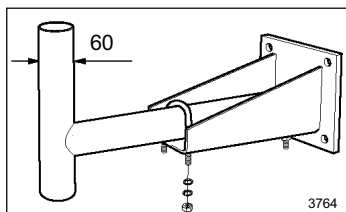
Комплект для монтажа на крыше/стене (изображен монтаж на стене)
